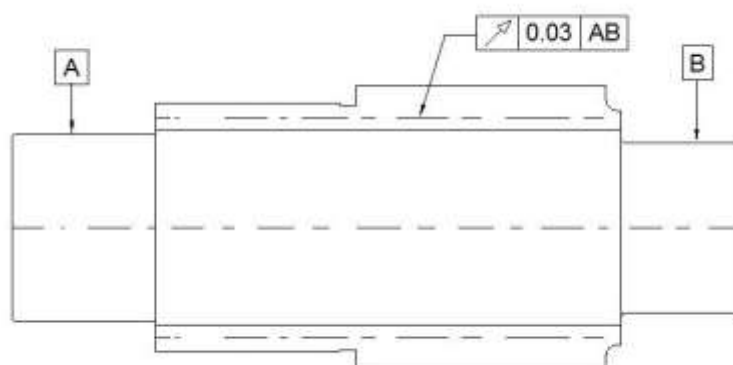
Dimenzijske tolerance valjastega zobnika
